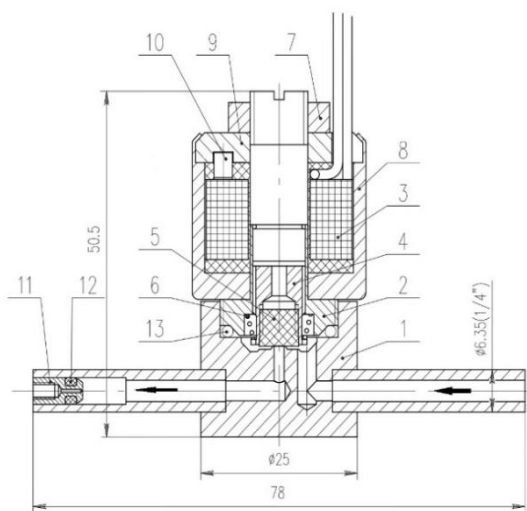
чертеж соленоидального клапана: 1 – корпус ; 3 – катушка; 4 – якорь, над которым расположен зазор электромагнита; 5 –уплотнитель (витон); 6 – возвратная пружина ; 8 – корпус катушки; 11, 12 – микродиафрагма.
